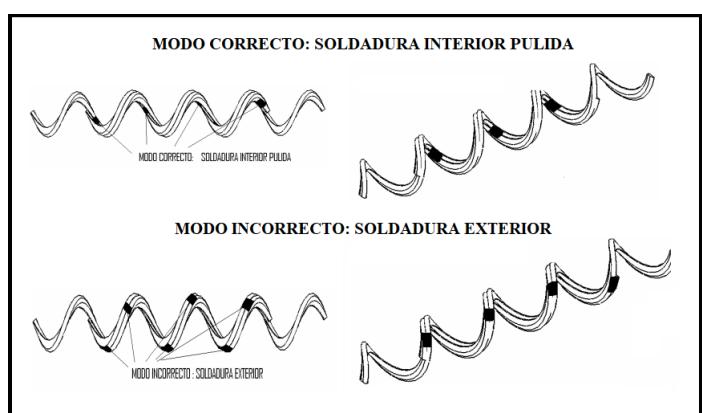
Soldaduras en un tornillo sinfín flexible. Fuente: [19].
